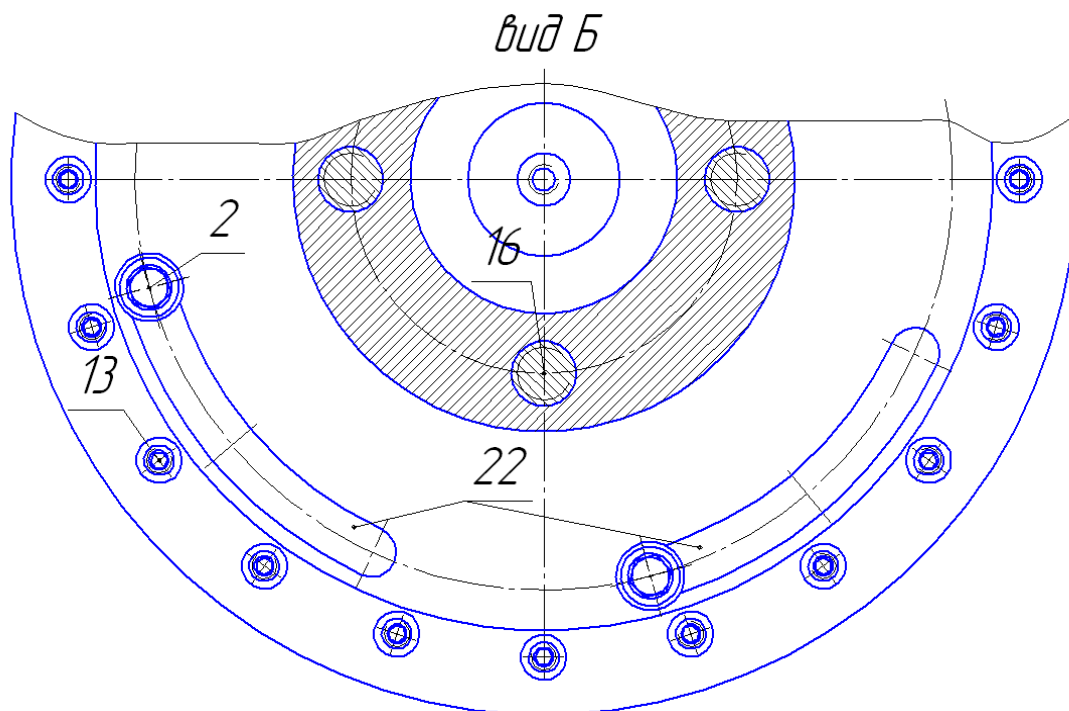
Вид торцевої фрези зі сторони шпинделя верстата
